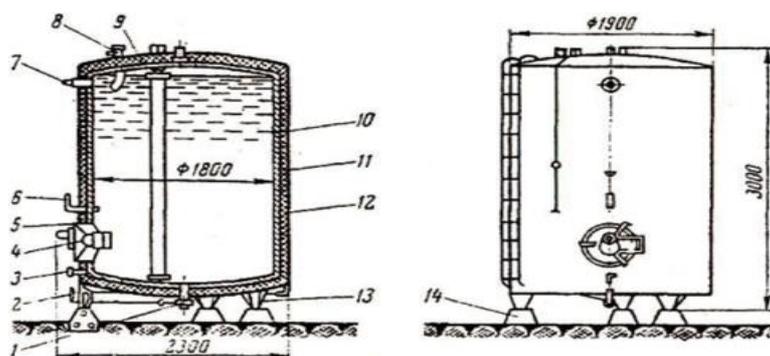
Резервуар РМВЦ-6 для хранения молока: 1- сливной кран; 2 - приспособление для открывания сливного крана; 3 -кран для отбора проб; 4 - привод мешалки; 5 - люк; 6 - оправа термометра; 7 - светильник; 8 - приемный патрубок; 9 - поплавков указателя уровня; 10 - корпус резервуара; 11 - изоляция; 12 - кожух; 13 - опоры резервуара; 14 - фундамент.
